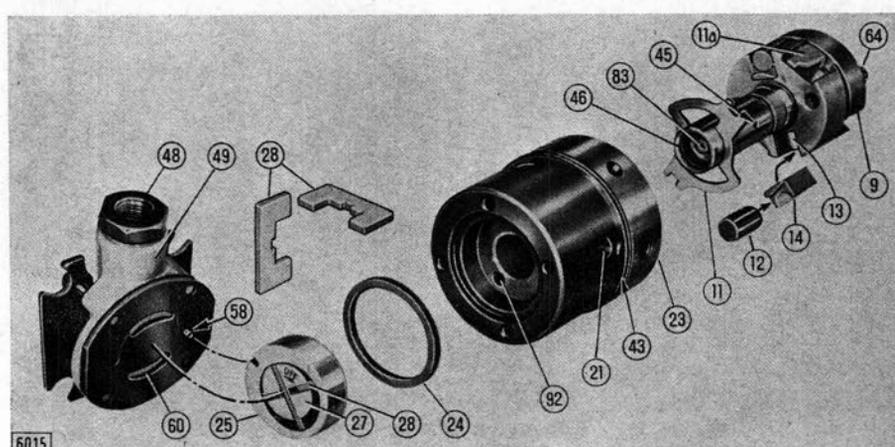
Vue de la pompe à palettes, tête hydraulique (23), rotor distributeur (46) et soupape de régulation de pression (49).
